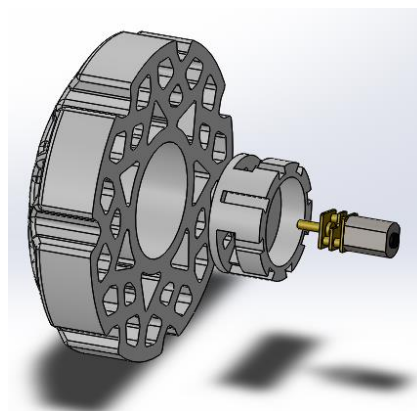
Modo de ensamblaje Rodadura-aro-motor
